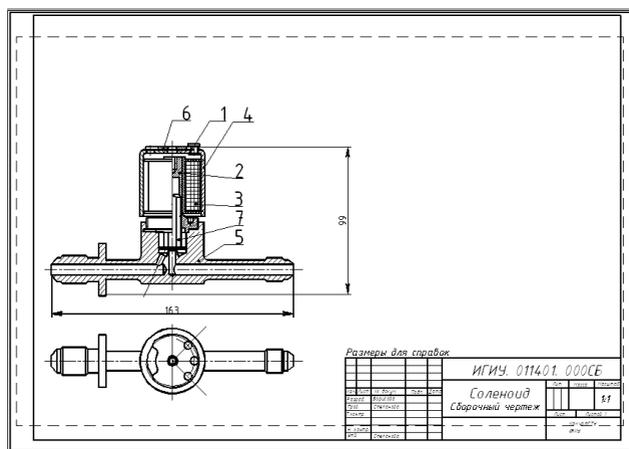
Сборочный чертеж изделия «Соленоид»
